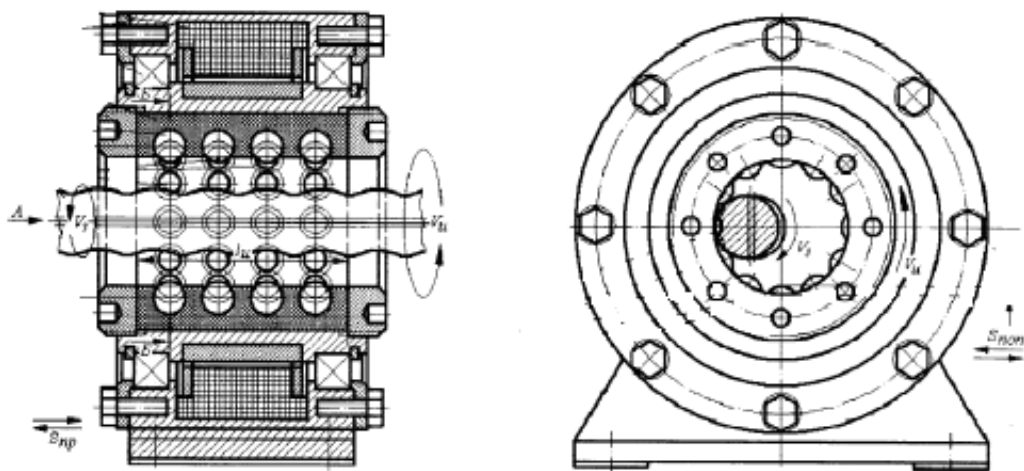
Схема пристосування для ударно-імпульсної обробки гвинтових поверхонь.
